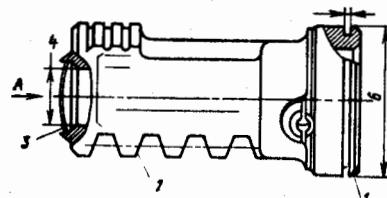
Основные дефекты рейки-поршня рулевого механизма автомобиля ЗИЛ-431410
